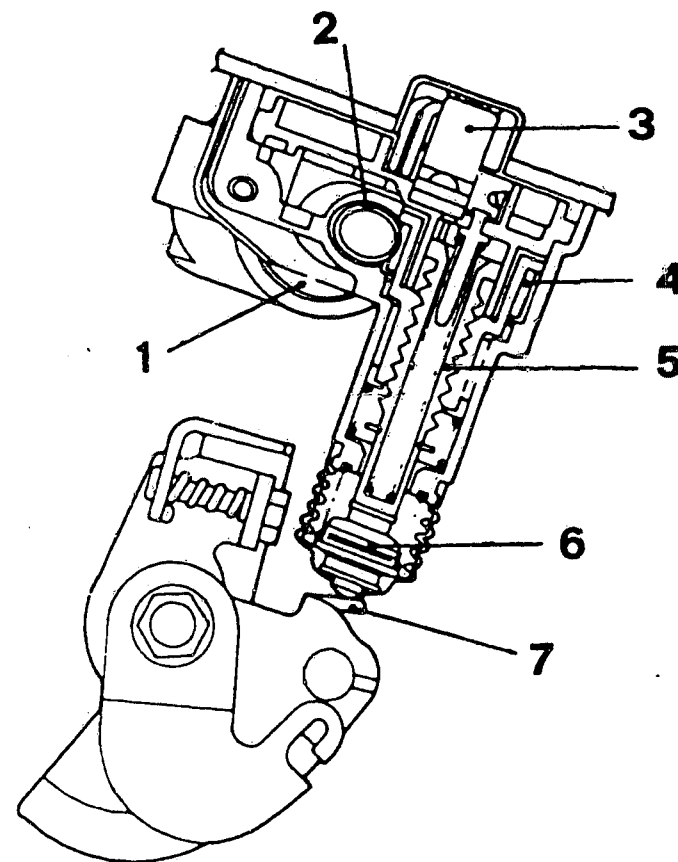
ISC-Schrittmotor im Schnitt: 1 Motor – 2 Schneckengetriebe – 3 Motorpositionssensor MPS – 4 Schneckenrad – 5 Kolben – 6 Leerlaufschalter – 7 ISC-Hebel.
